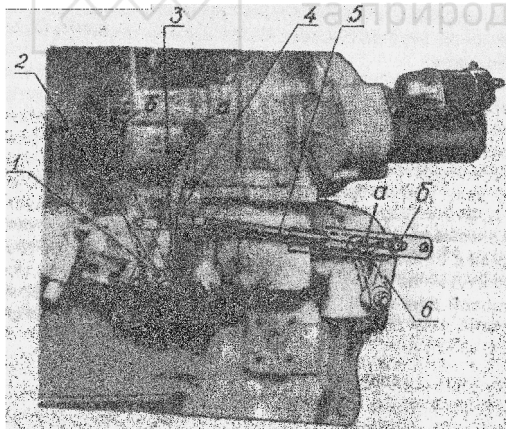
Регулювання механізму керування редуктором пускового двигуна: 1 - важіль включення муфти зчеплення редуктора; 2 - валик важеля включення муфти зчеплення редуктора; 3 - болт стяжний; 4 - палець; 5 - тяга; 6 - важіль включення пускової шестерні; а - важіль у положенні "включено"; б - важіль у положенні "виключено"
